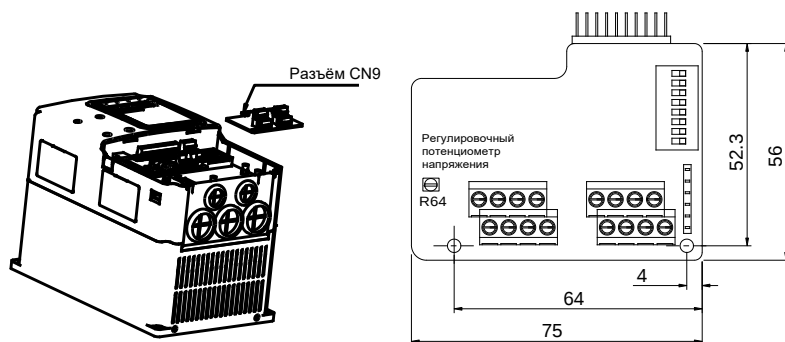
Схема установки и габаритные размеры карты PG асинхронного двигателя
